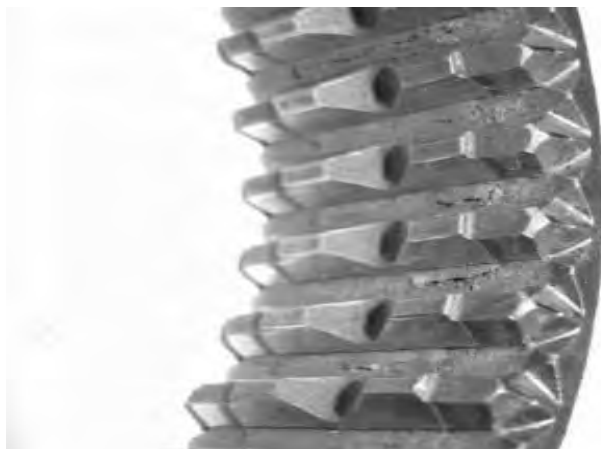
Конфигурация заходных кромок и форма боковых поверхностей зубьев подвижной зубчатой полумуфты
